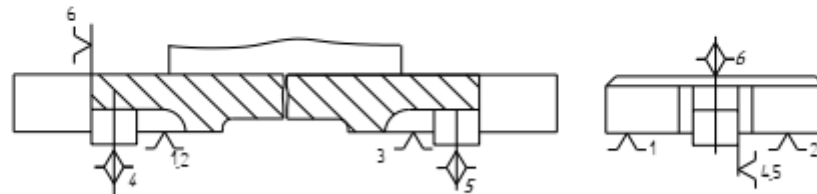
Принципова схема базування пристрою на верстаті
